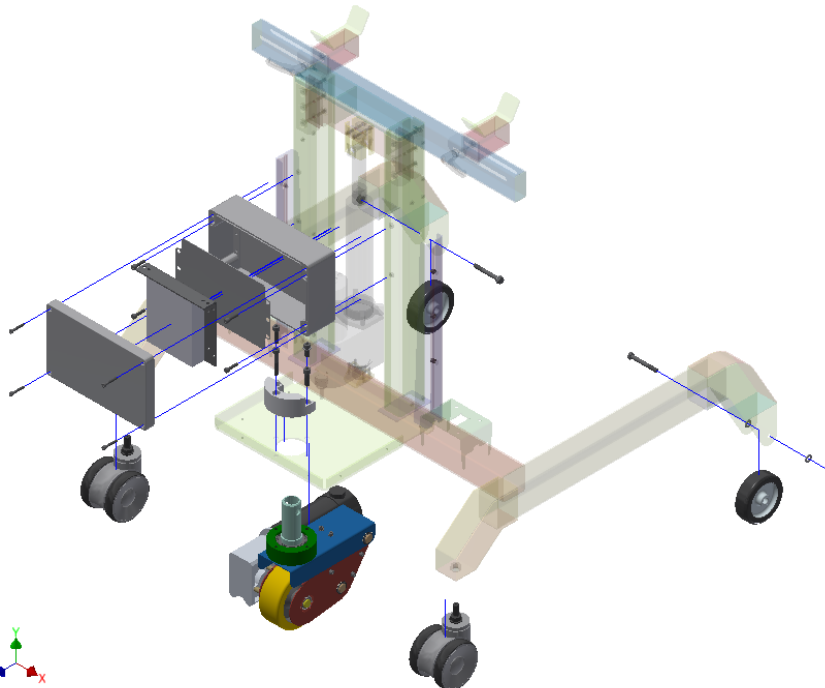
Vista explodida do conjunto 00014.1.002: 1) montagem da caixa de rolamentos; 2) montagem da parte inferior da estrutura e roda; 3) montagem do motor e acoplamento da parte superior à parte inferior
